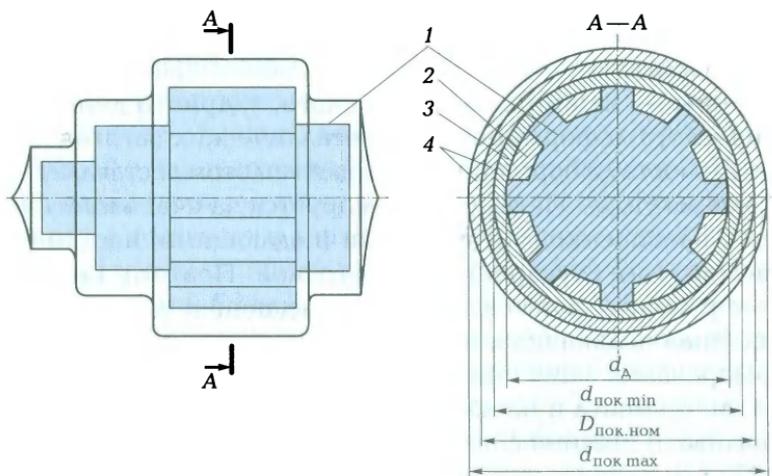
Чертеж поковки для детали с основными размерами, напуском, припуском и допуском:
